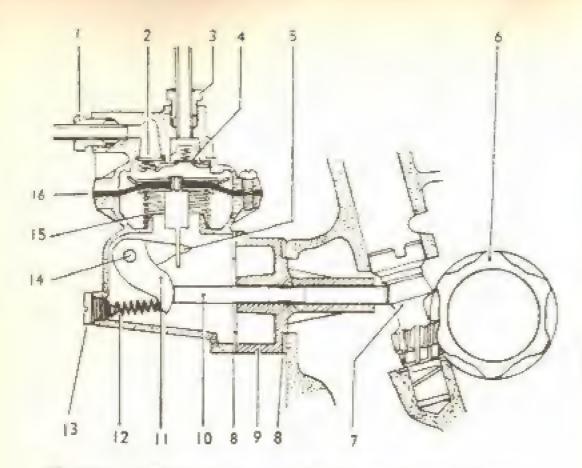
E - Corte da bomba de gasolina. (Motor "1 200" - 36 HP)
